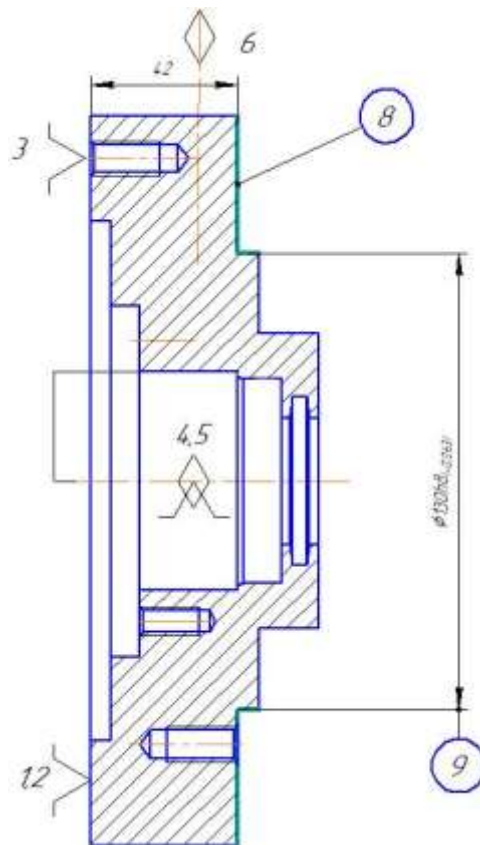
Ескіз механічної обробки із схемою базування (операція 030)
